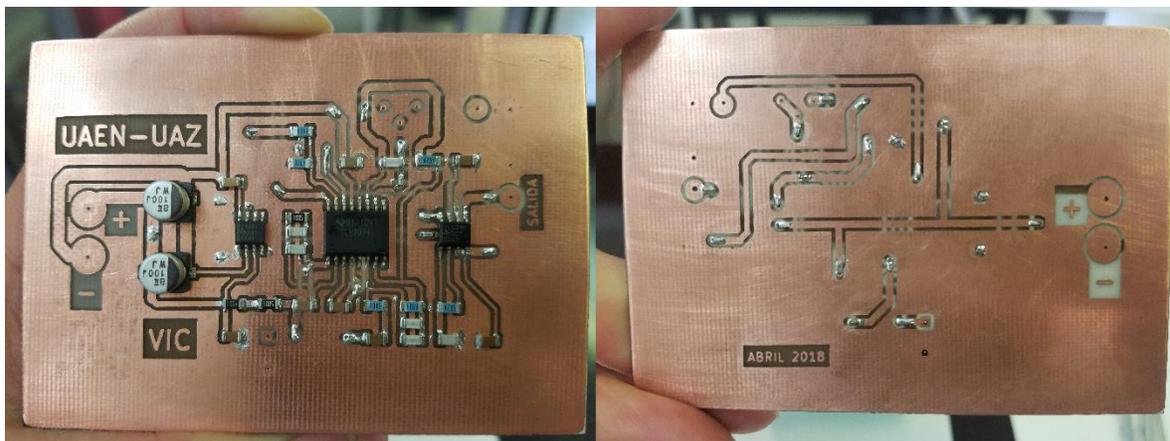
Circuito impreso doble cara con componentes soldados
